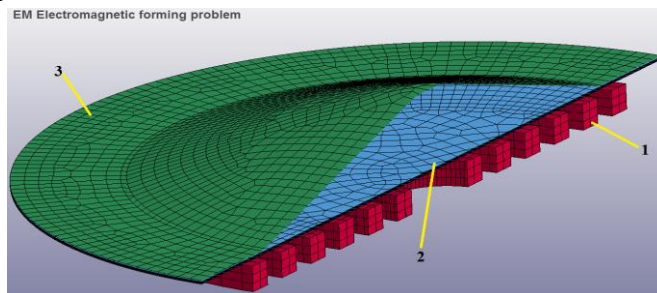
Продольное сечение конечно-элементного моделирования с шестью витками катушки: 1 – катушка; 2 – заготовка; 3 – матрица.
